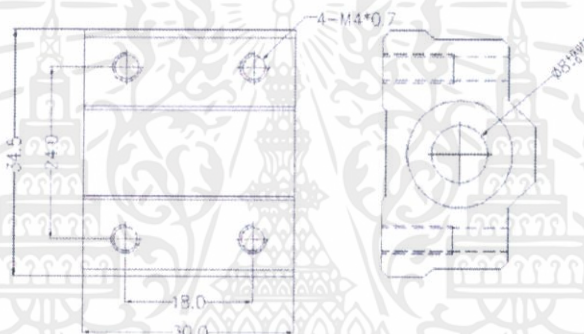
Linear shaft, Linear shaft support, Linear bearing slider
